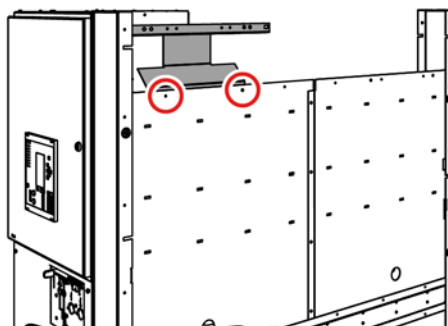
Точки крепления короткой металлической пластины для защиты от аварийной электрической дуги
